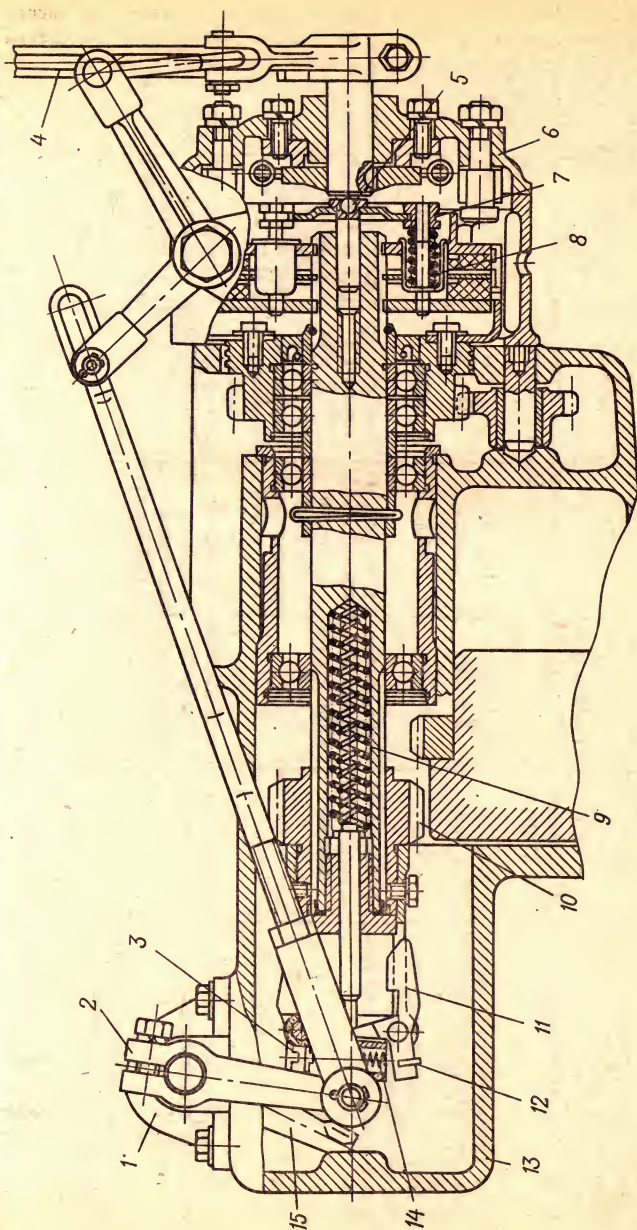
Механизм силовой передачи пускового двигателя дизеля Д-65Н:
